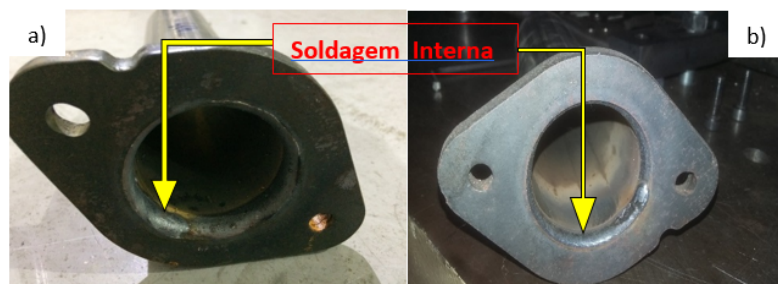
a) Corpo de prova soldado internamente com arame sólido. b). Corpo de prova soldado internamente com arame tubular.
